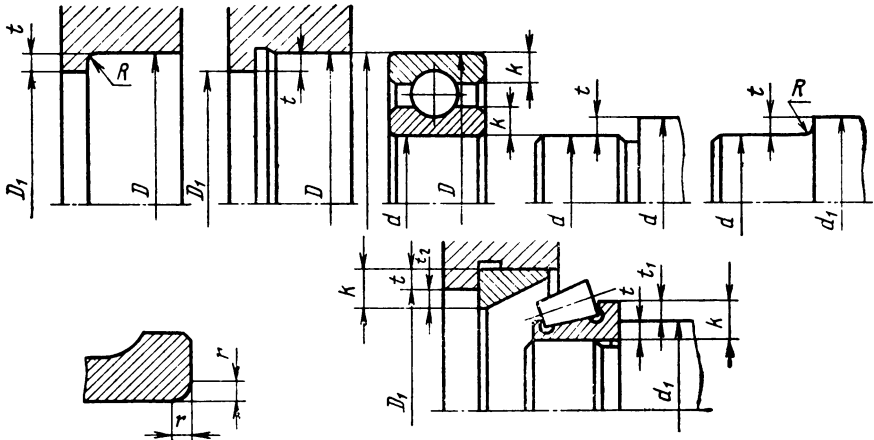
Упорные буртики на валах и в отверстиях корпусов
